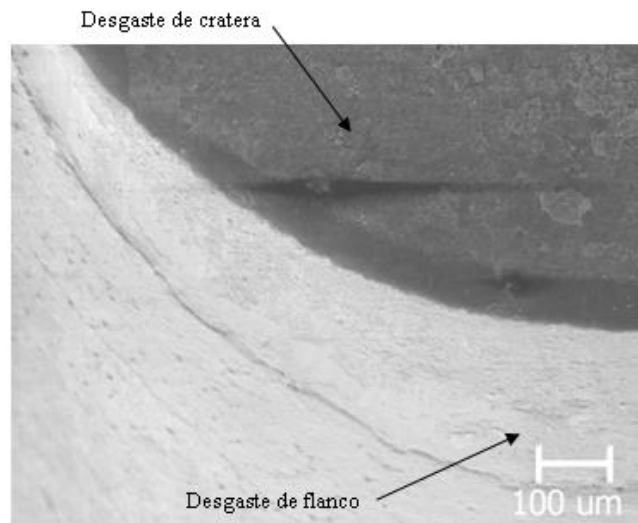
Desgaste apresentado pela ferramenta revestida com CrAlN durante usinagem a seco das barras de aço.
